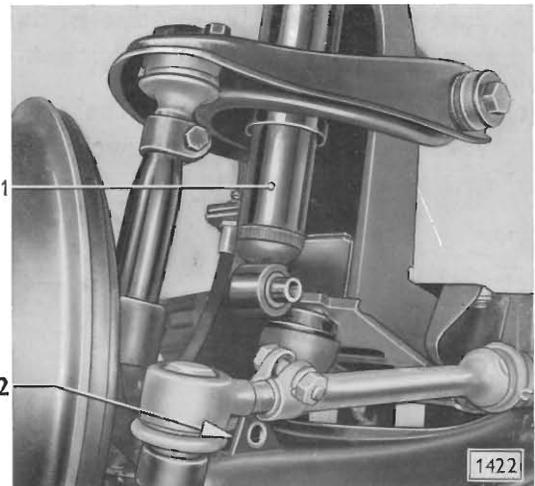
Stoßdämpfer aus unterer Befestigung gelöst und hochgeschoben
